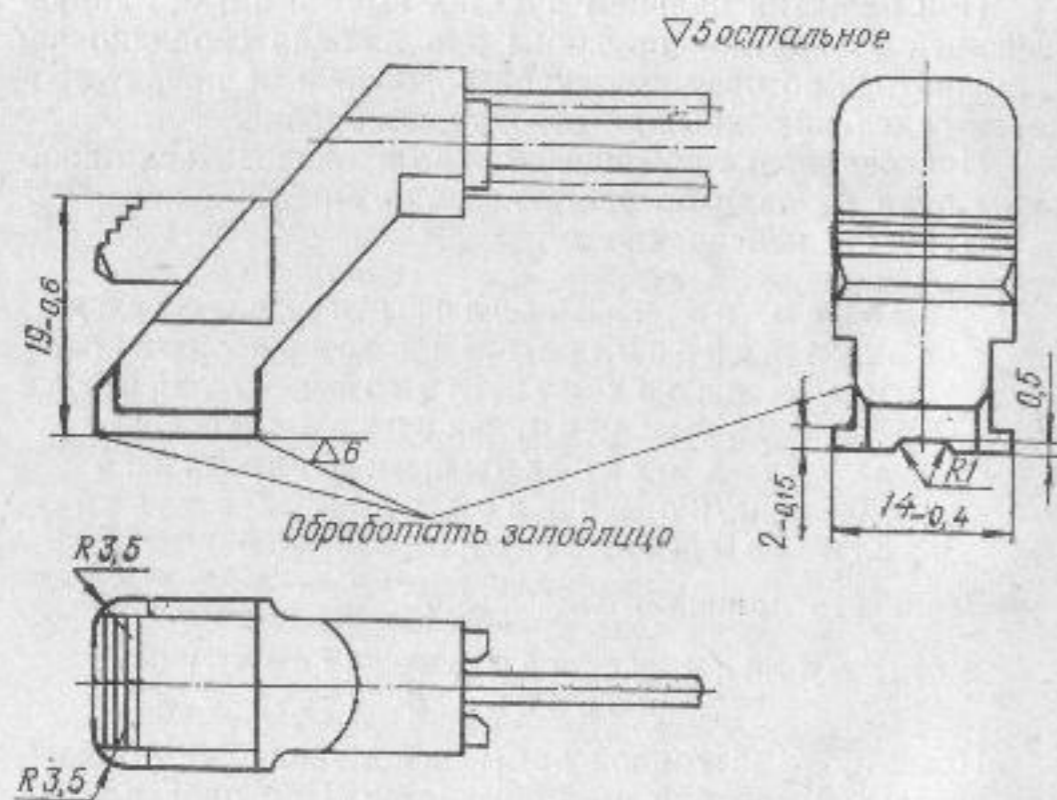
Обработка выступов пятки направляющей возвратной пружины после наплавки
